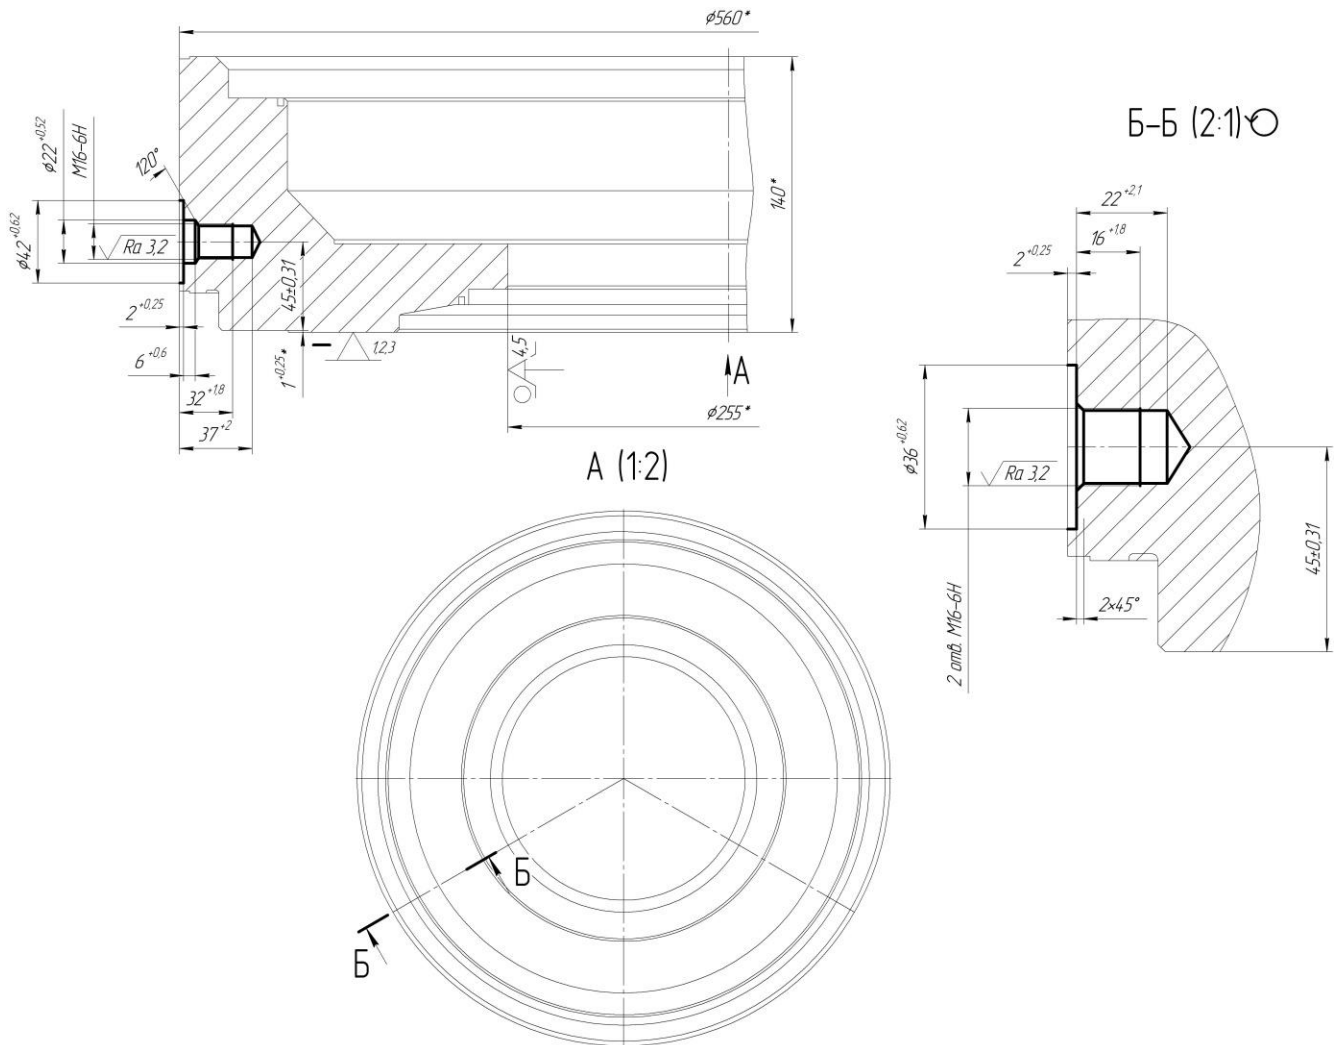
Схема базування заготовки на комплексній операції (перший варіант)
